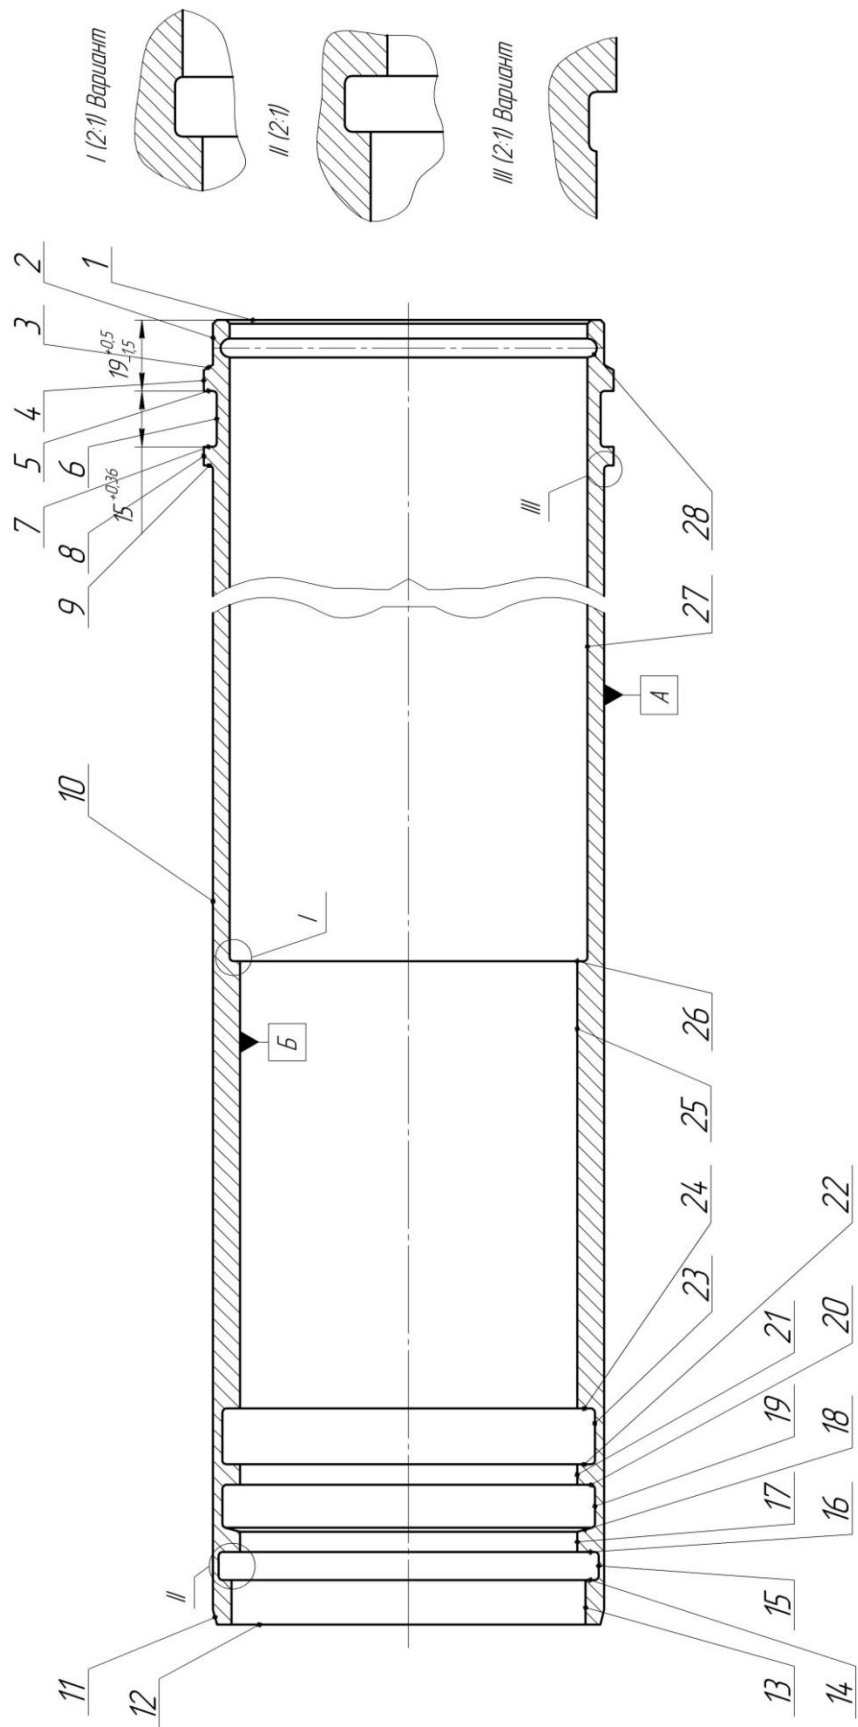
Деталь - «Плунжер», кодированный чертеж
